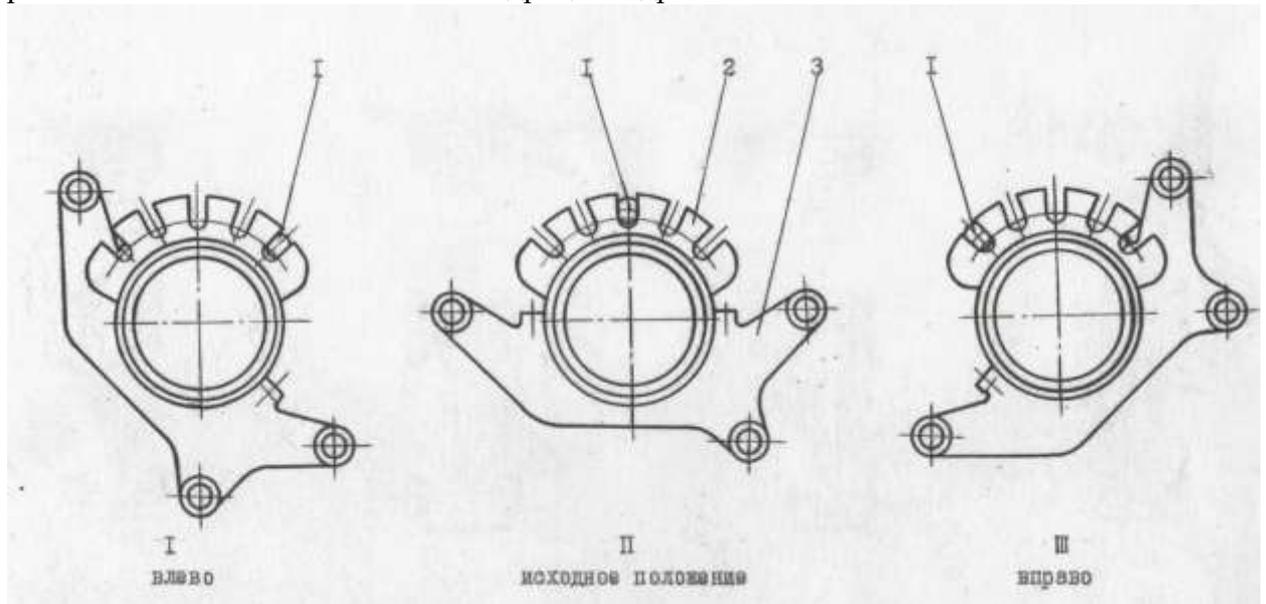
Положение поворотного кронштейна подвески гидроцилиндров при установке отвала под углом до 90°
